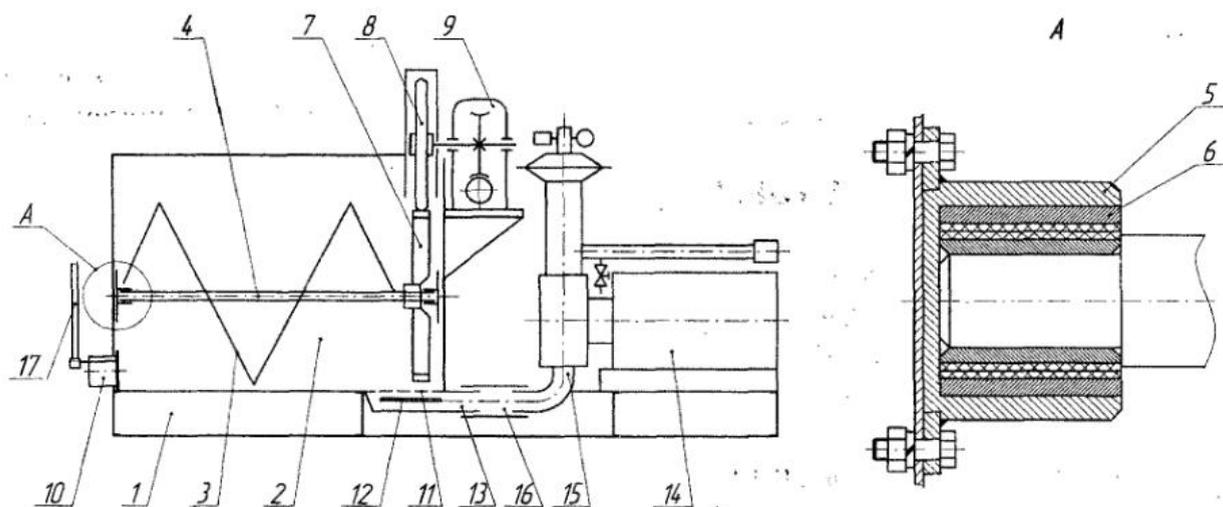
Схематичні перерізи установки РЗУ-04 та опори кінця вала для механічної мішалки
